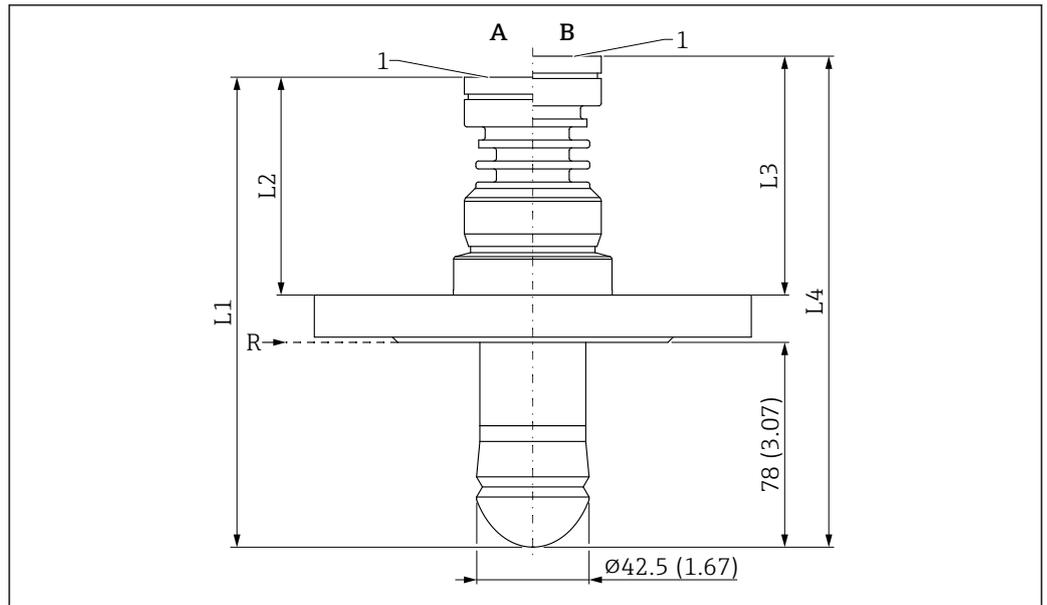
法兰过程连接的外形尺寸示意图。测量单位 mm (in)
